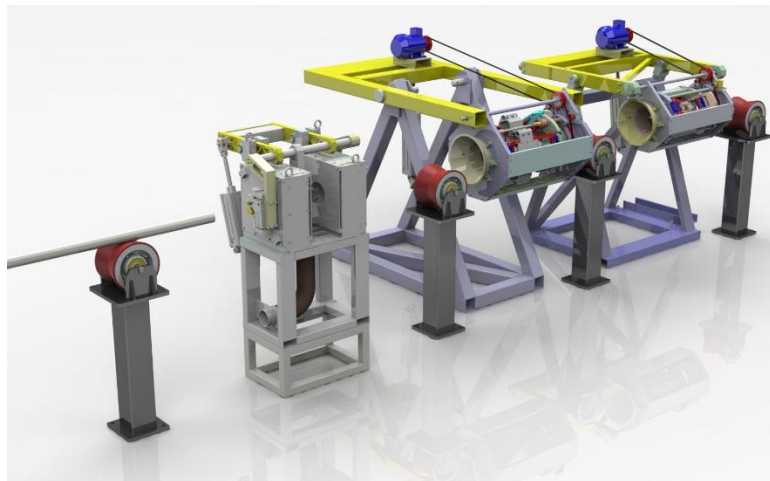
Внешний вид установки «УРАН–3000Д–НКТ» для автоматического неразрушающего контроля НКТ
